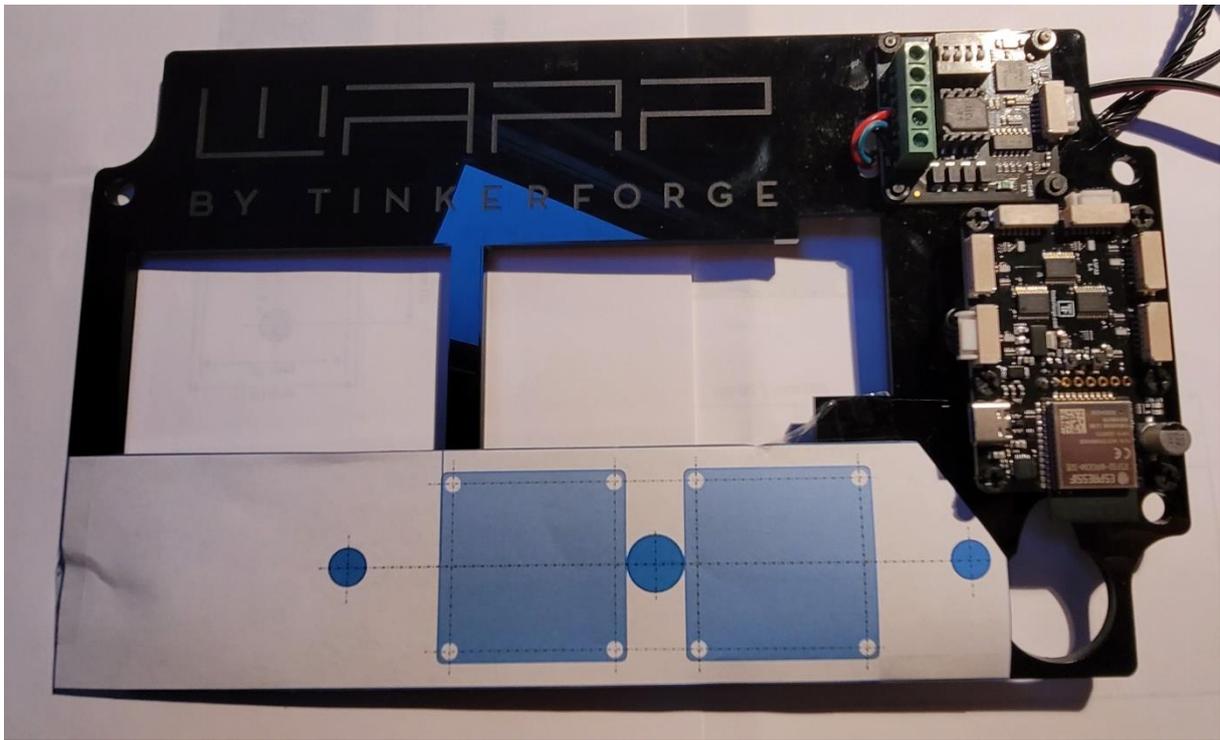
befestigte Bohrschablone auf innerer Abdeckung
